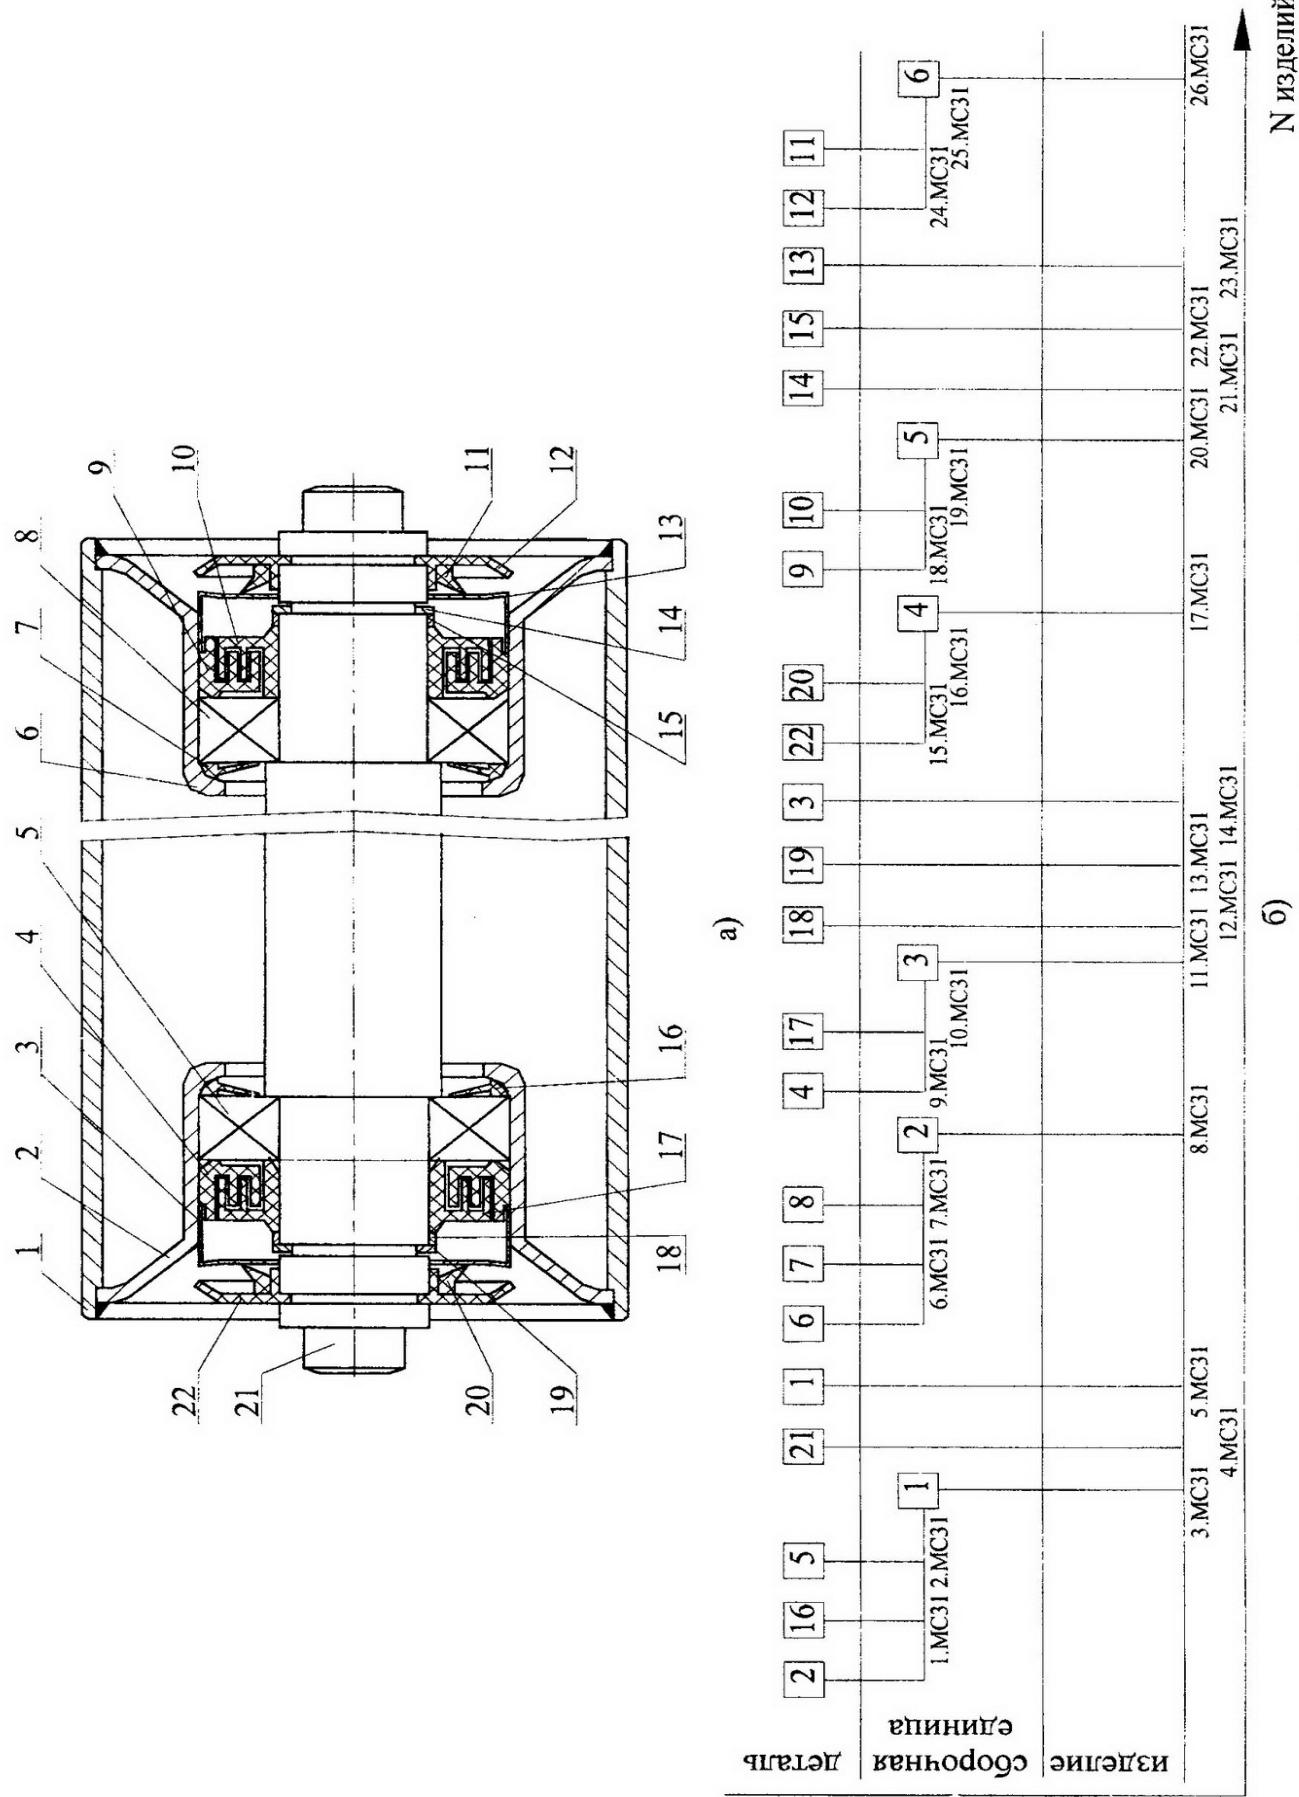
Ролик ленточного конвейера (а) и схема сборки (б):
